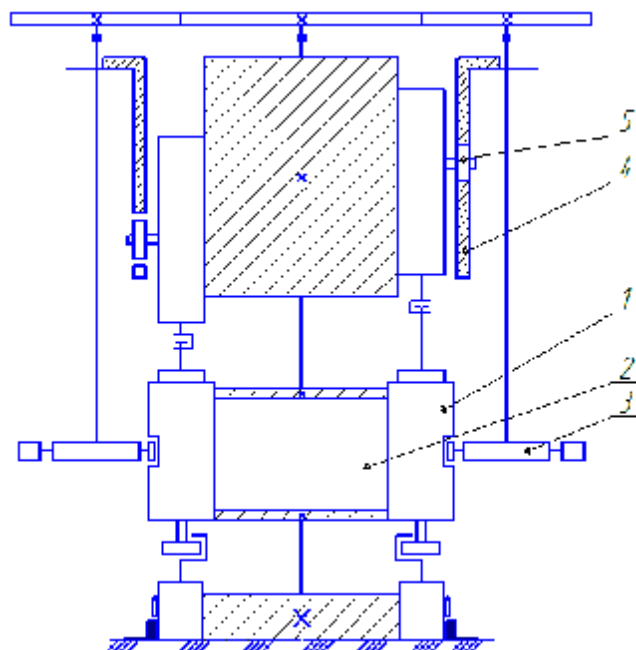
Схема роторной машины с кулачковым приводом верхнего инструмента и гидравлическим – нижнего: 1- инструментальный блок; 2 – технологический ротор; 3 – транспортный ротор; 4 – цилиндрический пазовый кулачок; 5- ролик.
